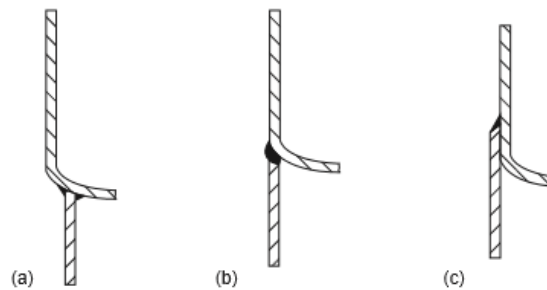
Soldaduras en un recipiente tipo falda. (a) al cabezal inferior (b) a ras de la carcasa (c) al exterior de la carcasa. Fuente: (1)
